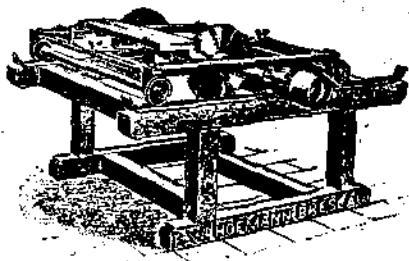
Станок с двумя круглыми пилами для укорачивания клепок.
